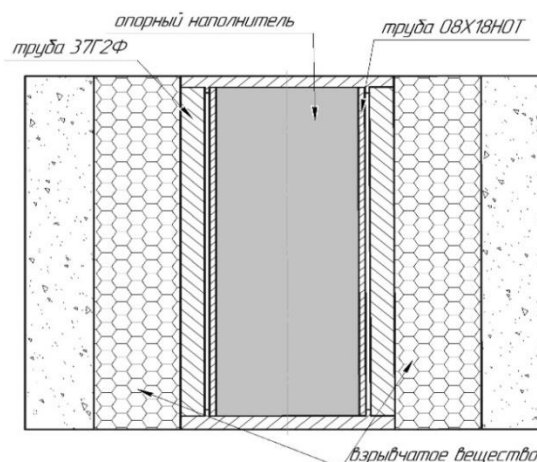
Экспериментальная схема сварки взрывом двухслойных трубных заготовок с применением опорных элементов
